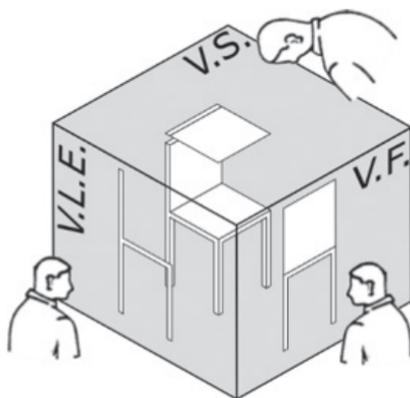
| Projeções das vistas nos planos de projeção no 1º diedro
